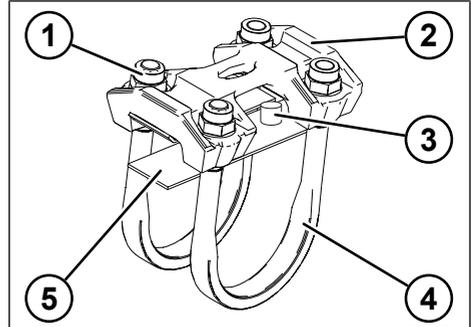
Bauteile der Einbindung (Luftfederlenker oben)
